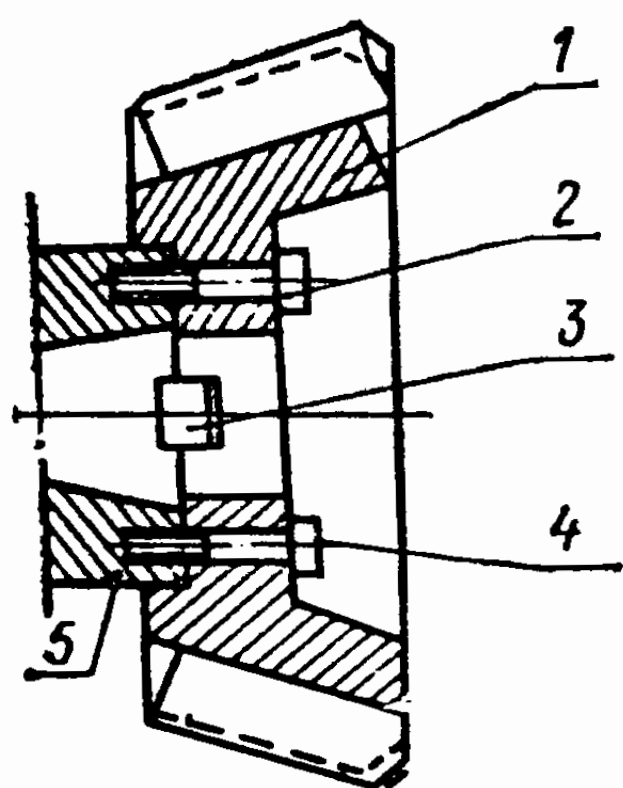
Закрепление торцовых фрез на шпинделе фрезерного станка.
